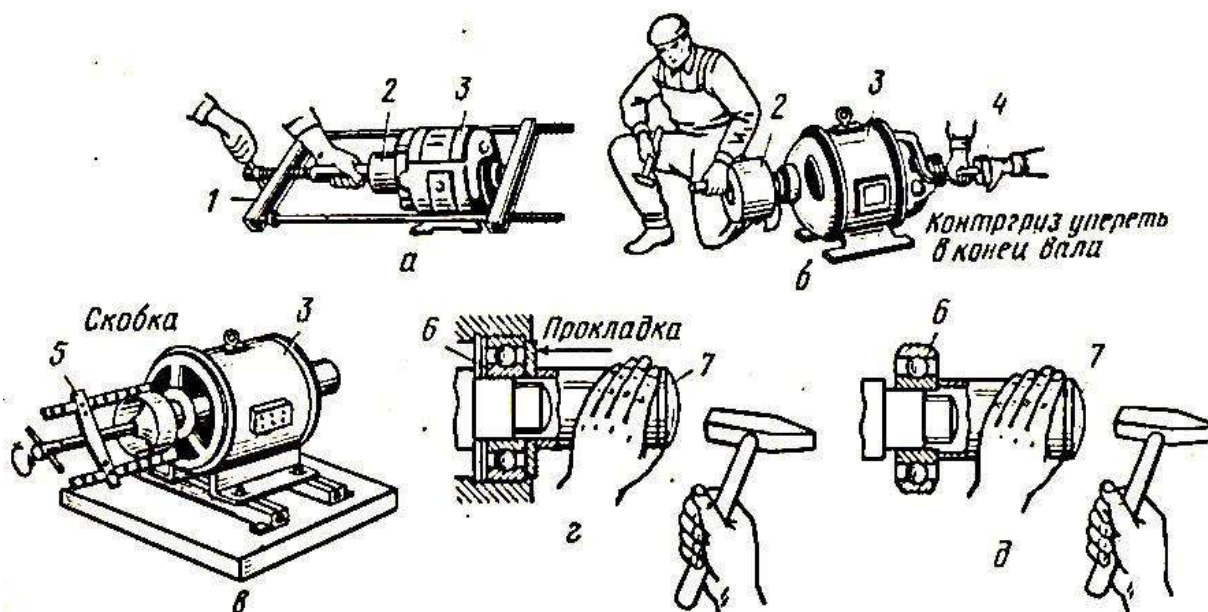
Способы насадки шкивов и подшипников на вал:
